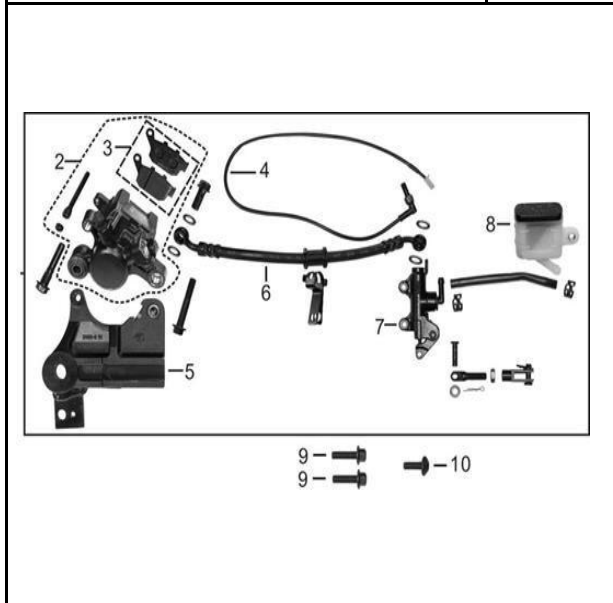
CALIPER Y BOMBA DE FRENO TRASERO
